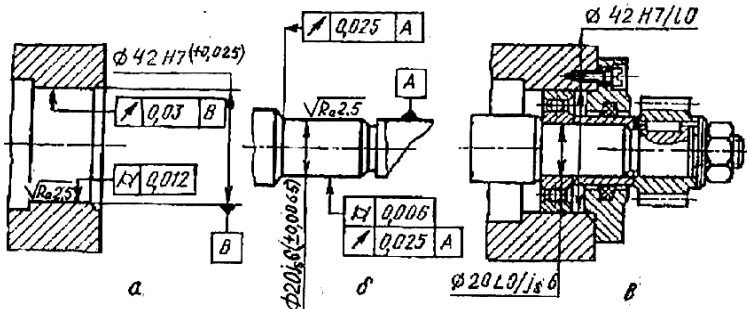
Обозначение допусков и посадок подшипников качения на чертежах: *a* – отверстия; *b* – вала; *c* – подшипникового узла в сборе
